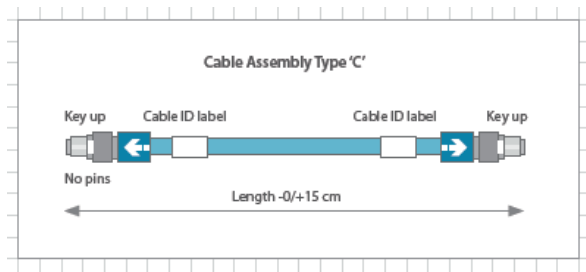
Cabo de inter-ligação tipo "C" do sistema MT Connect
